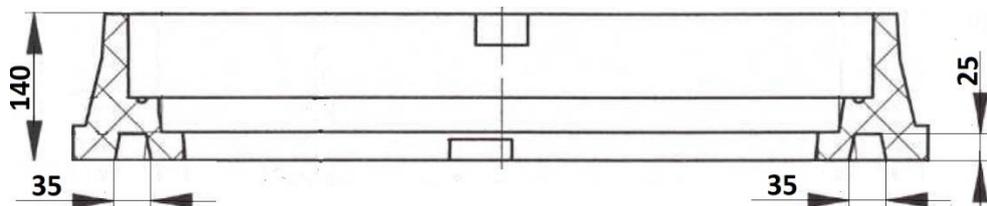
Размеры выемок в корпусе люка ППЛ.
